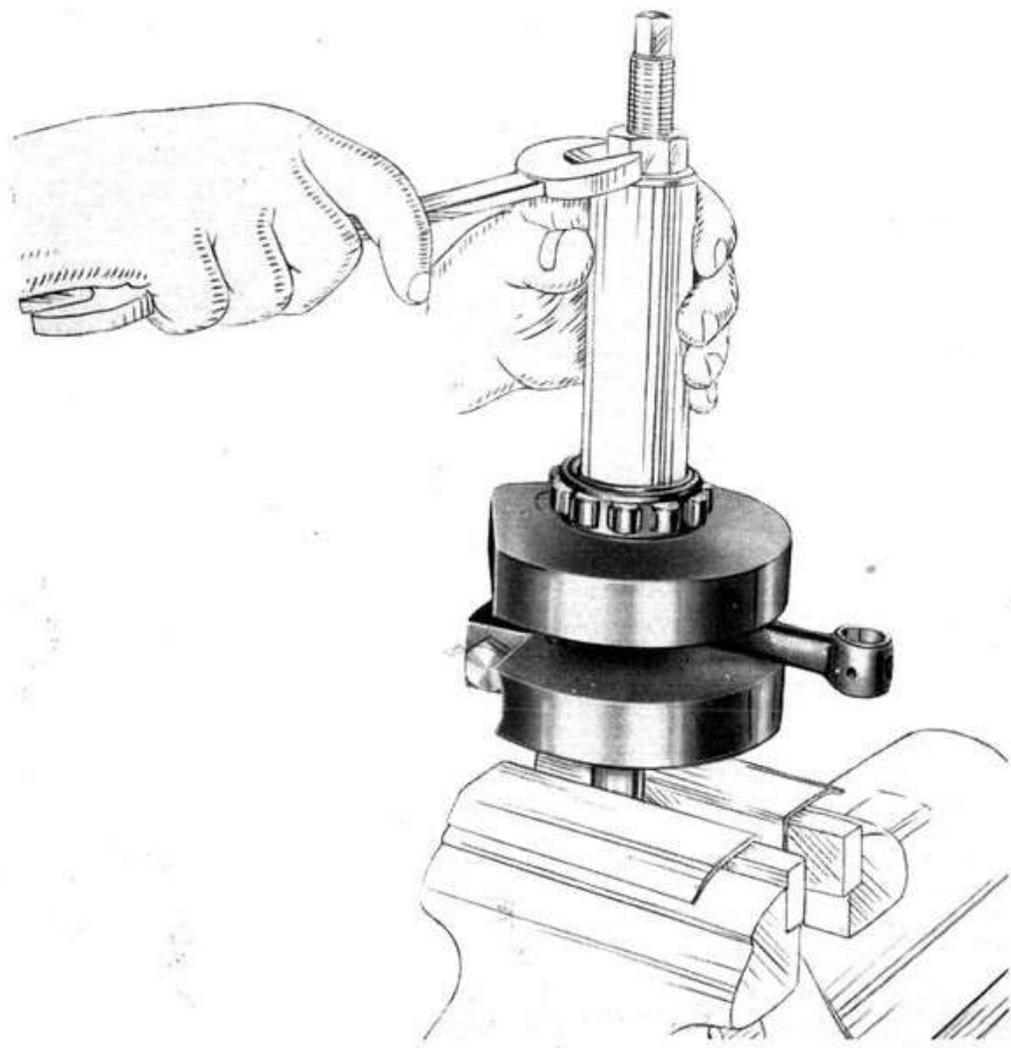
Montaggio del cuscinetto a rulli sull'albero motore.
